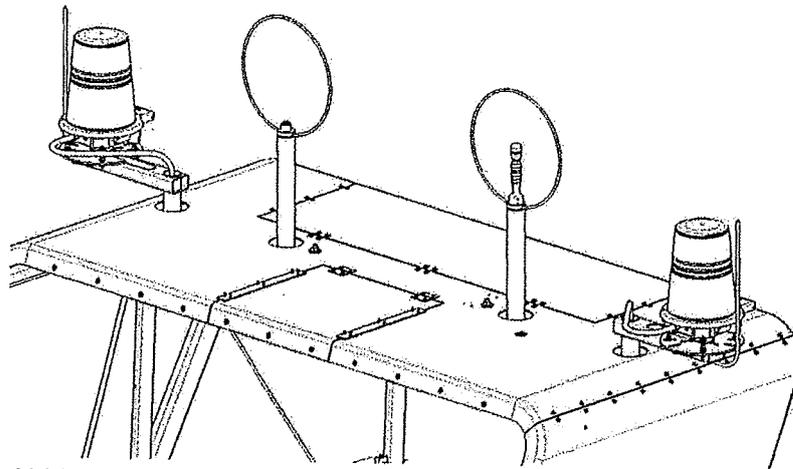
Ultraschall-Anemometer und Gefahrenfeuer an der Rückseite des Maschinenhauses.
